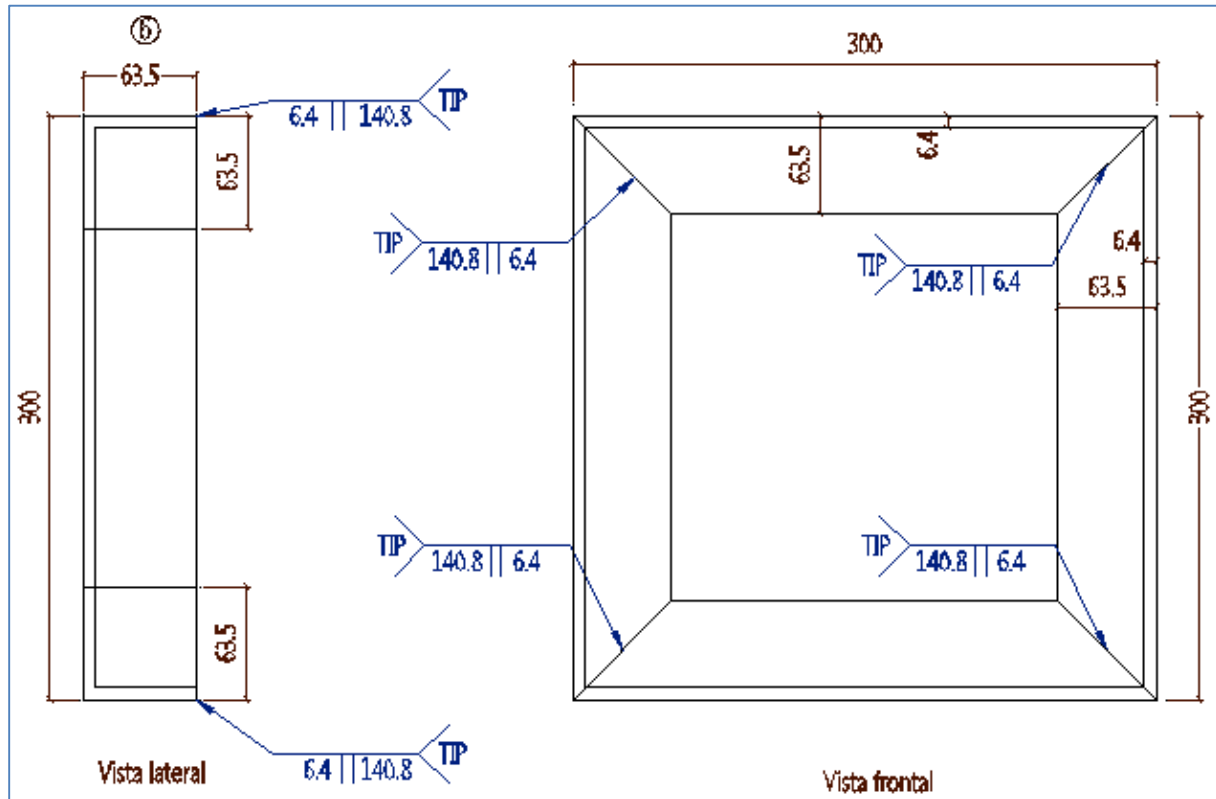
Detalle despiece pieza No.6 modelo 3 tensión.
